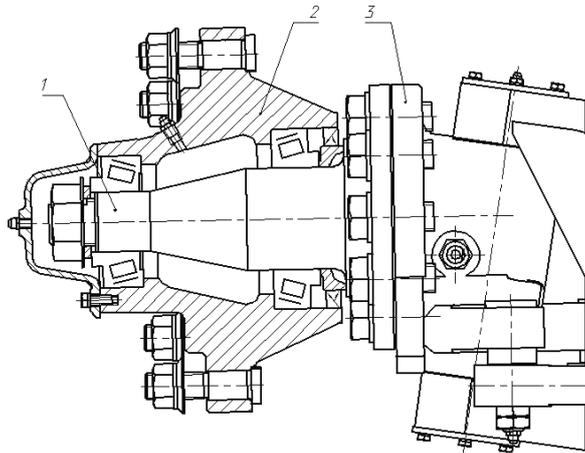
Разъемный поворотный кулак комбайна КЗС-1218: 1 – ось кулака; 2 – ступица; 3 – поворотный кулак
